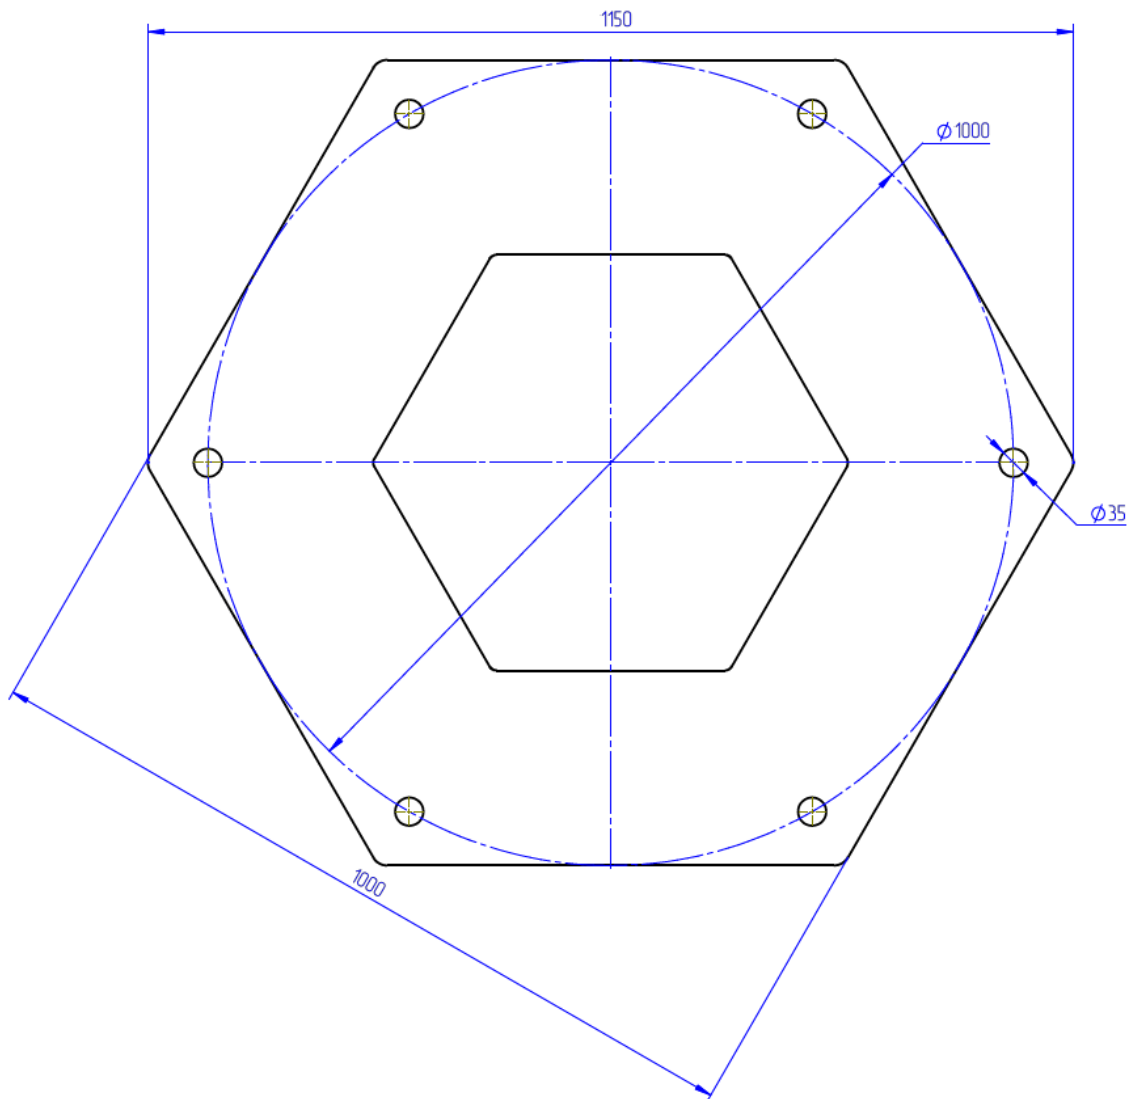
Крепление ОПУ к фундаменту/площадке
